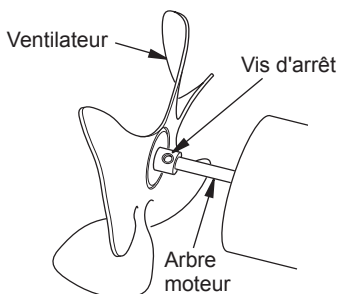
Emplacement du ventilateur, de l'arbre moteur et des vis d'arrêt
